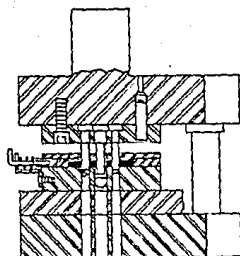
VISTA DE LA SECCION FRONTAL DE LA
